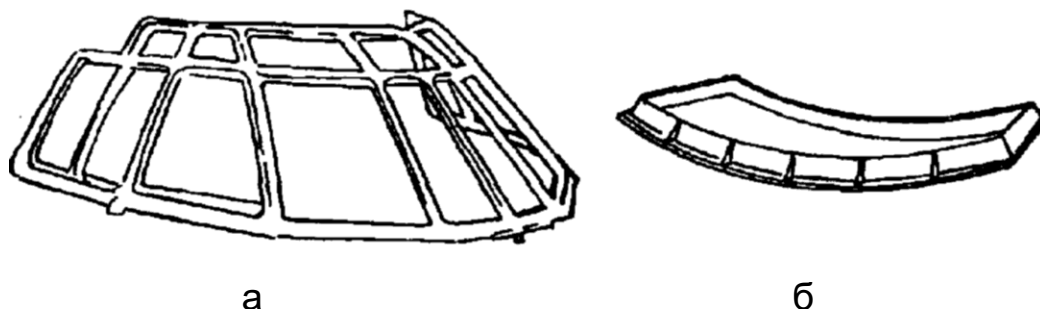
Типовые детали каркаса фюзеляжа, обрабатываемые на пятикоординатных станках с ЧПУ:
